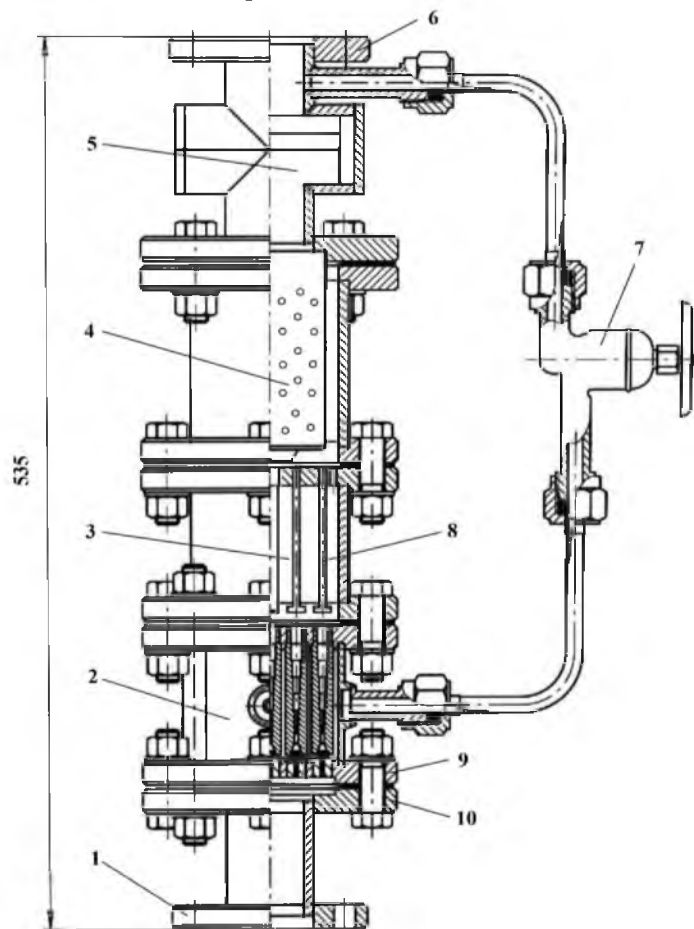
Схема четырёхкамерного гомогенизатора для приготовления ВТЭ:
